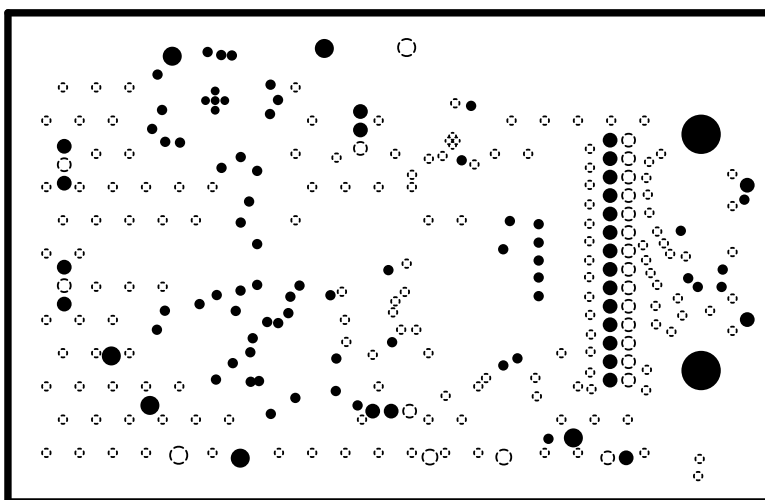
ADS1282EVM 的 PCB 布局 (内部 GND 平面)
